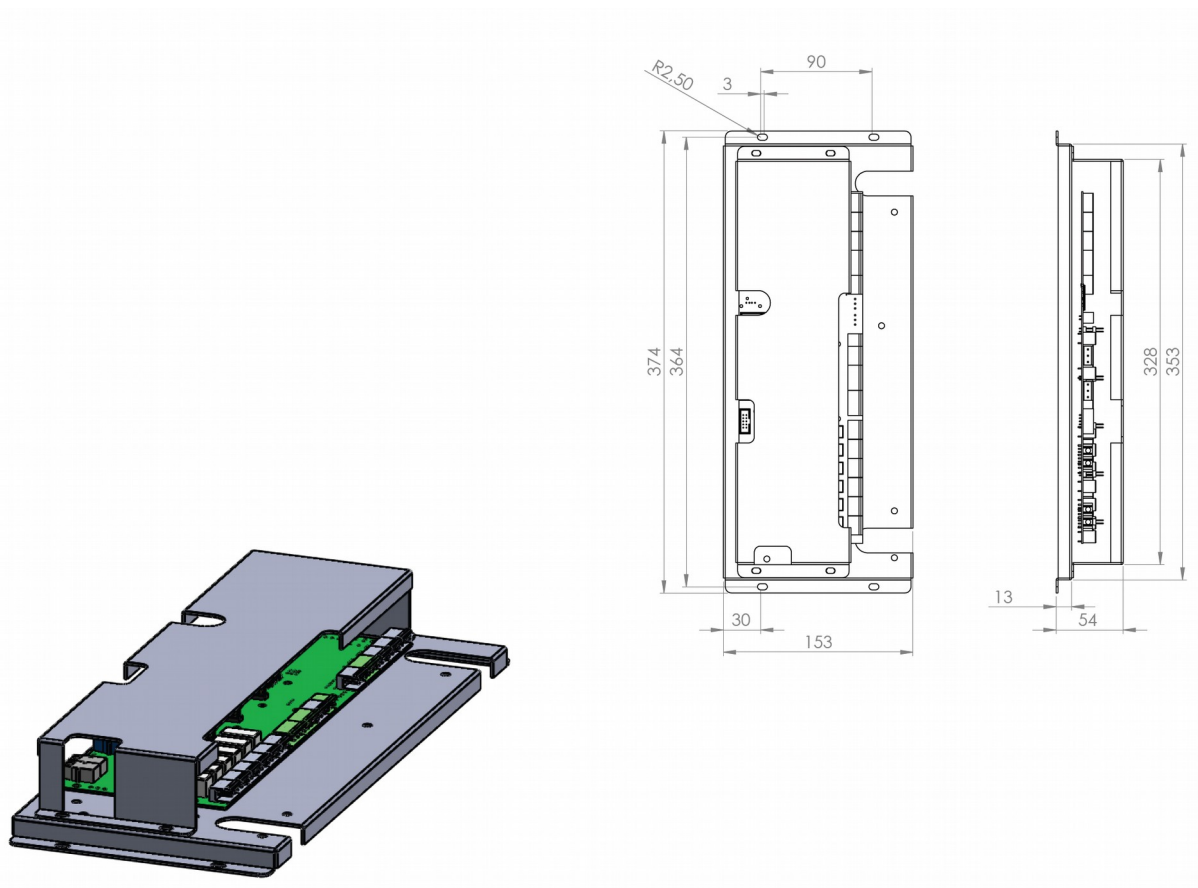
Модуль 3/3 — плата I/O PCB MFC1000/11
